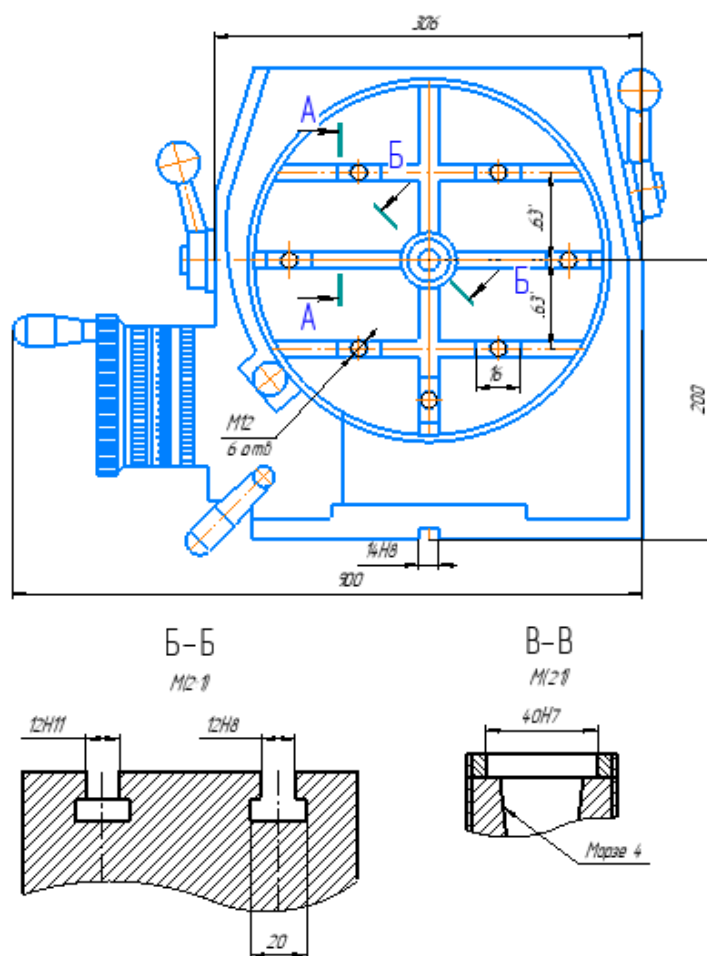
Стіл поворотний горизонтально-вертикальний.
